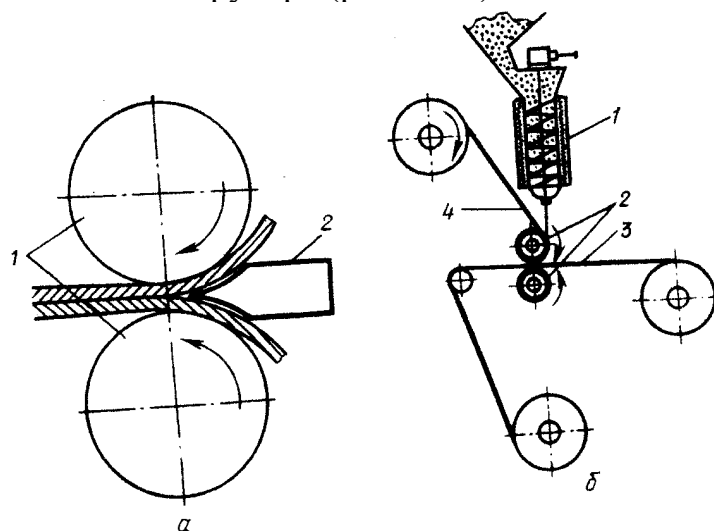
Принципы сварки: а – клиновой способ: 1 – прессовые валы; 2 – тепловой клин; б – с помощью расплава: 1 – экструдер для нитевидного расплава; 2 – прессовые валы; 3 – бумага; 4 – фольга
